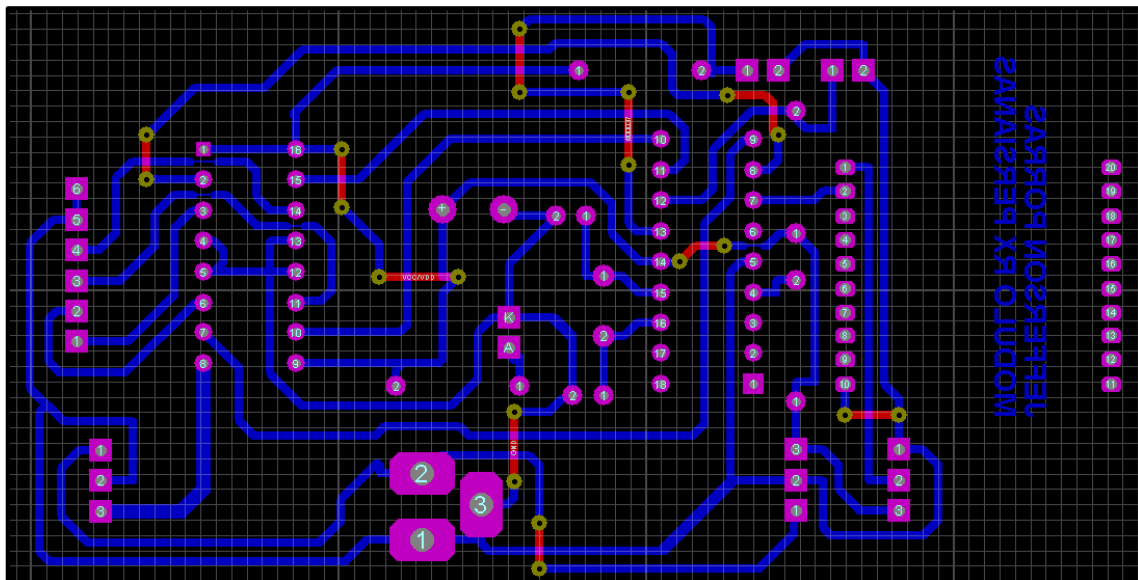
Diseño PCB Módulo Receptor Persianas.
